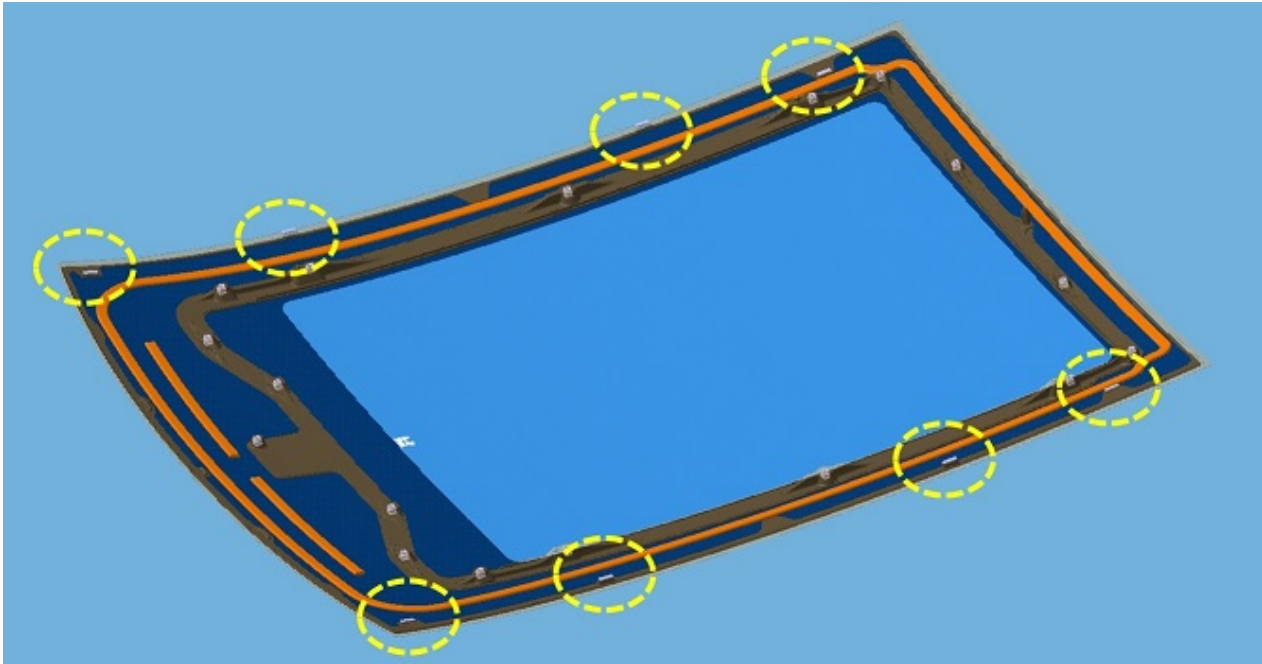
8 Distanzhalter (Ansicht Dachunterseite, siehe gelbe Kreise)
